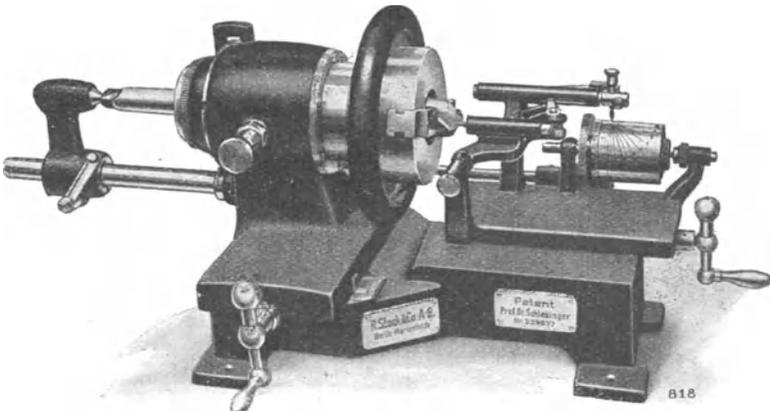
Spiralbohrerspitzen-Meßmaschine.
